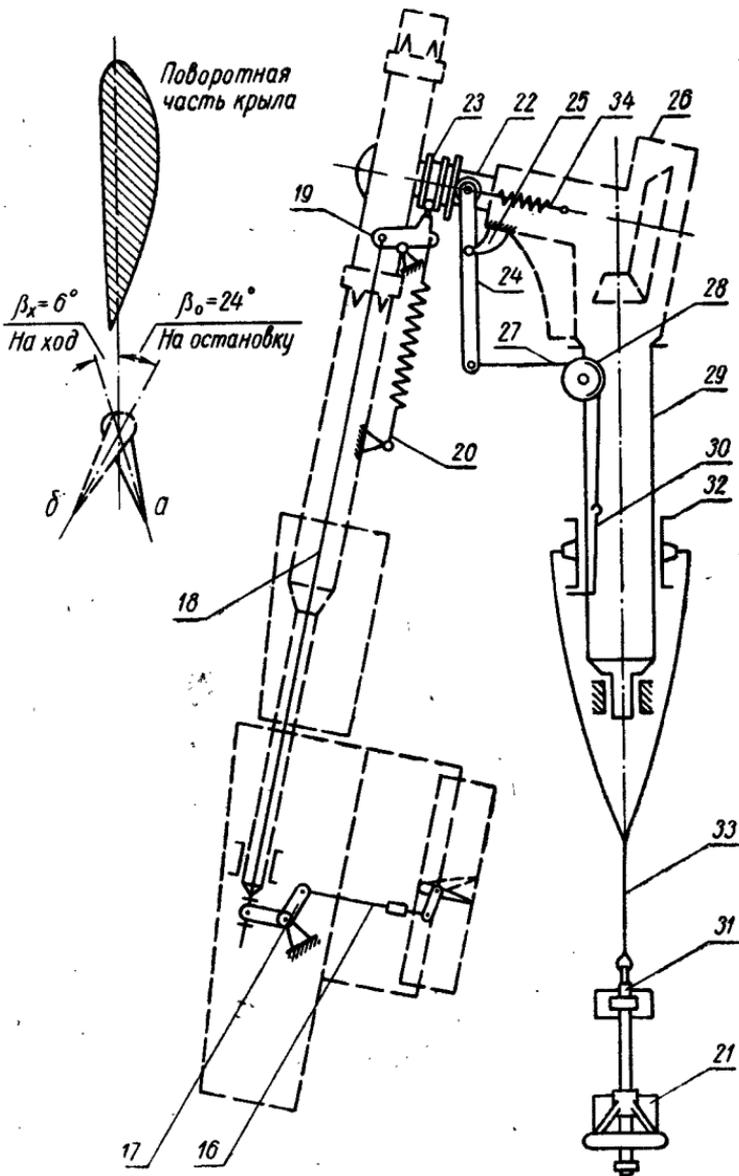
Кинематическая схема головки ветродвигателя Д-12:
